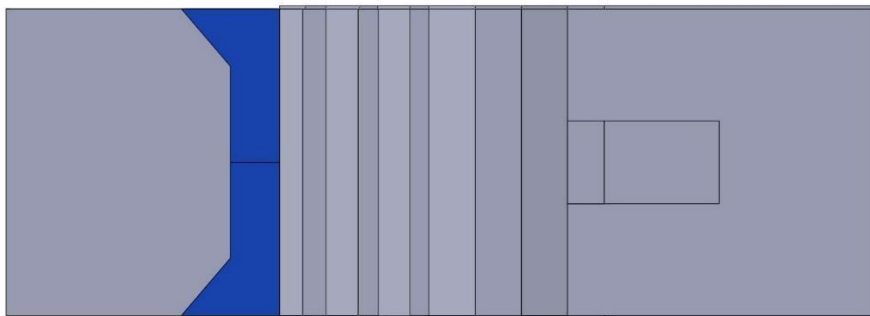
Vista em planta do modelo desenhado em SolidWorks®.
